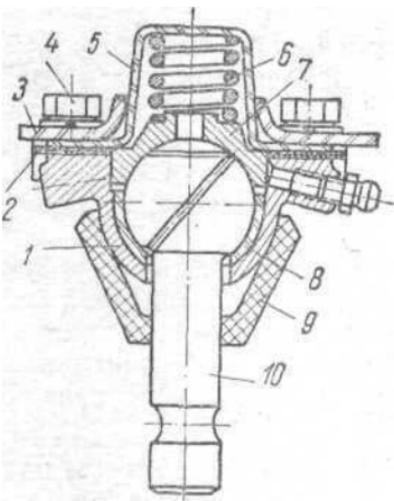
Верхний шаровой шарнир стойки передней подвески автомобиля модели 403: 1 — корпус; 2 — регулировочные прокладки; 3 — верхний рычаг; 4 — болт; 5 — крышка; 6 — пружина; 7 — нажимной вкладыш; 8 — опорный вкладыш; 9 — защитный чехол; 10 — шаровой палец
